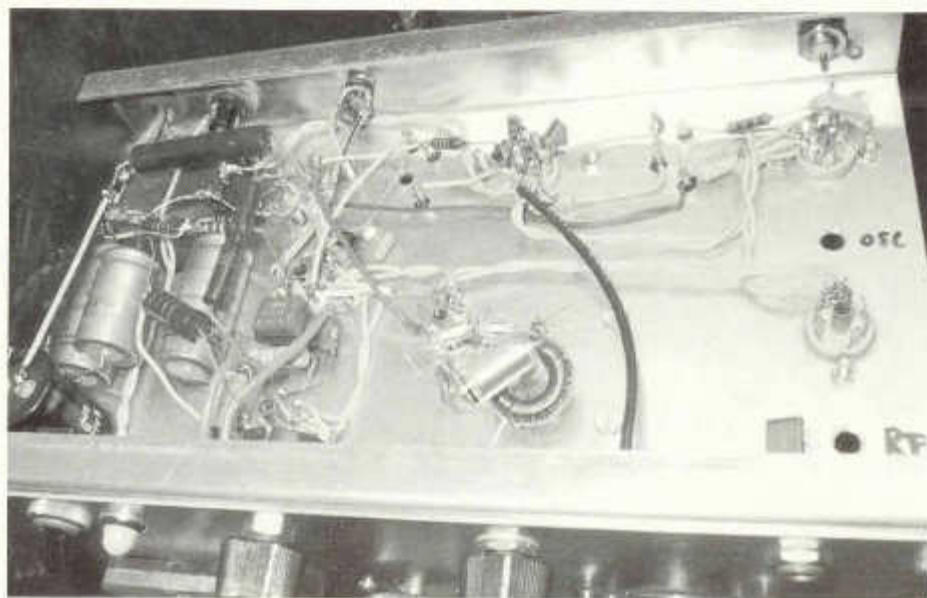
Ansicht von unten. Die Verdrahtung wurde in konventioneller Technik, ohne gedruckte Schaltung durchgeführt.
